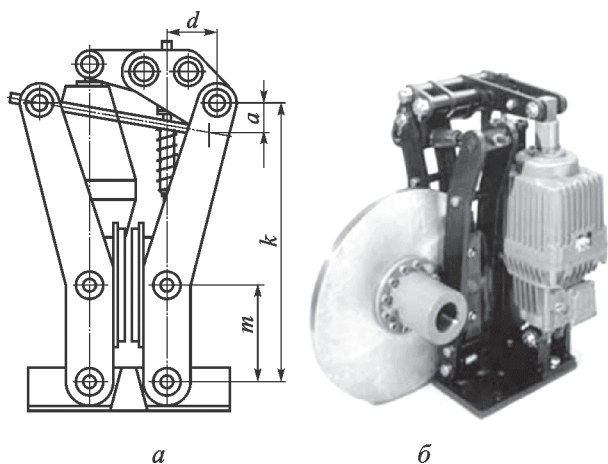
Конструктивная схема (а) и общий вид (б) дисково-колодочного тормоза с рычажной системой и электрогидравлическим приводом производства Magnetek Inc. (США)
